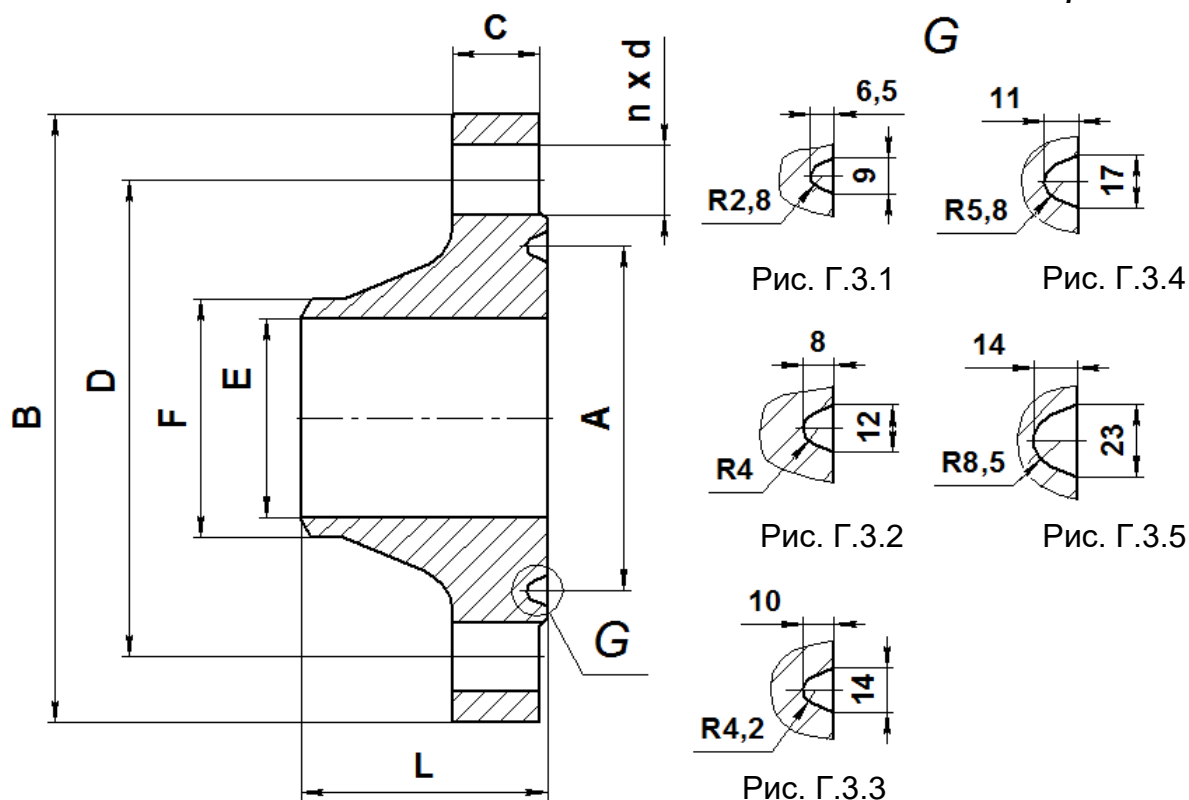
Размеры фланцев КМЧ для преобразователей исполнения «С» с давлением 10 - 25 МПа и исполнением уплотнительной поверхности «J»
